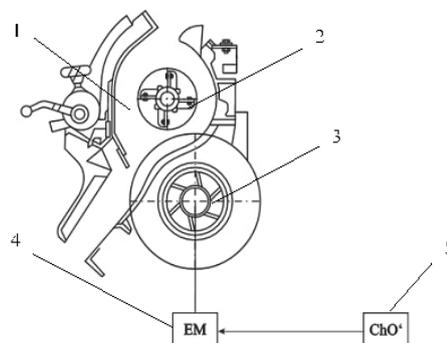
Рабочая камера линтерной машины с регулируемой скоростью пильного цилиндра
